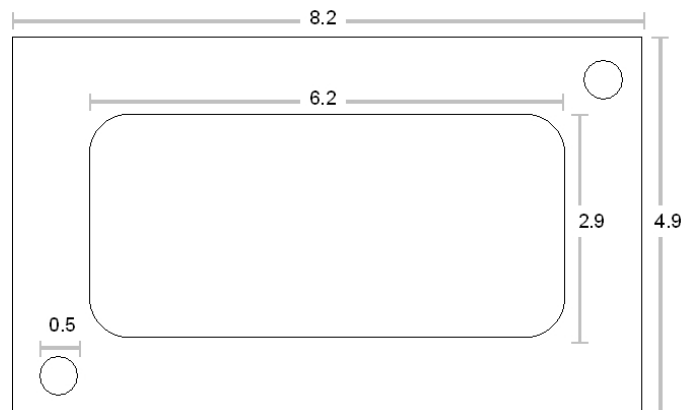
Plano de pieza inferior del molde para la vulcanización de muestras. Dimensiones en centímetros.
